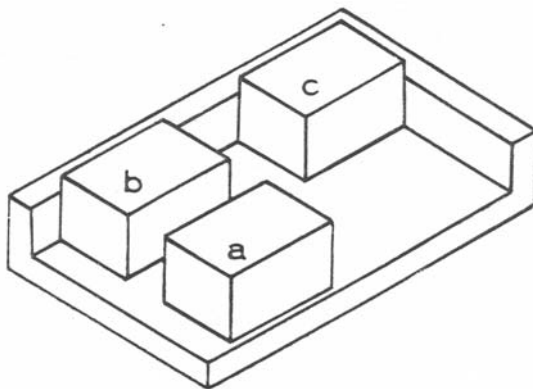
İş parçası boyutları ve yerleştirme boyutları [72]
